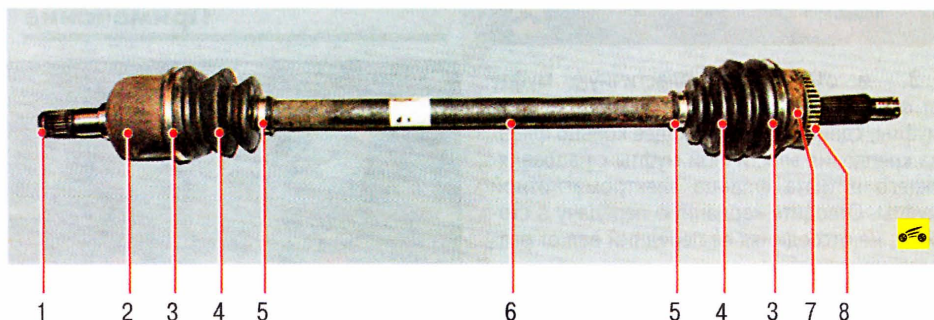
Привод заднего колеса: 1 — стопорное кольцо; 2 — внутренний шарнир равных угловых скоростей; 3 — большие хомуты крепления чехлов шарниров; 4 — чехлы шарниров; 5 — малые хомуты крепления чехлов шарниров; 6 — вал привода; 7 — наружный шарнир равных угловых скоростей; 8 — задающее кольцо датчика частоты вращения колеса
